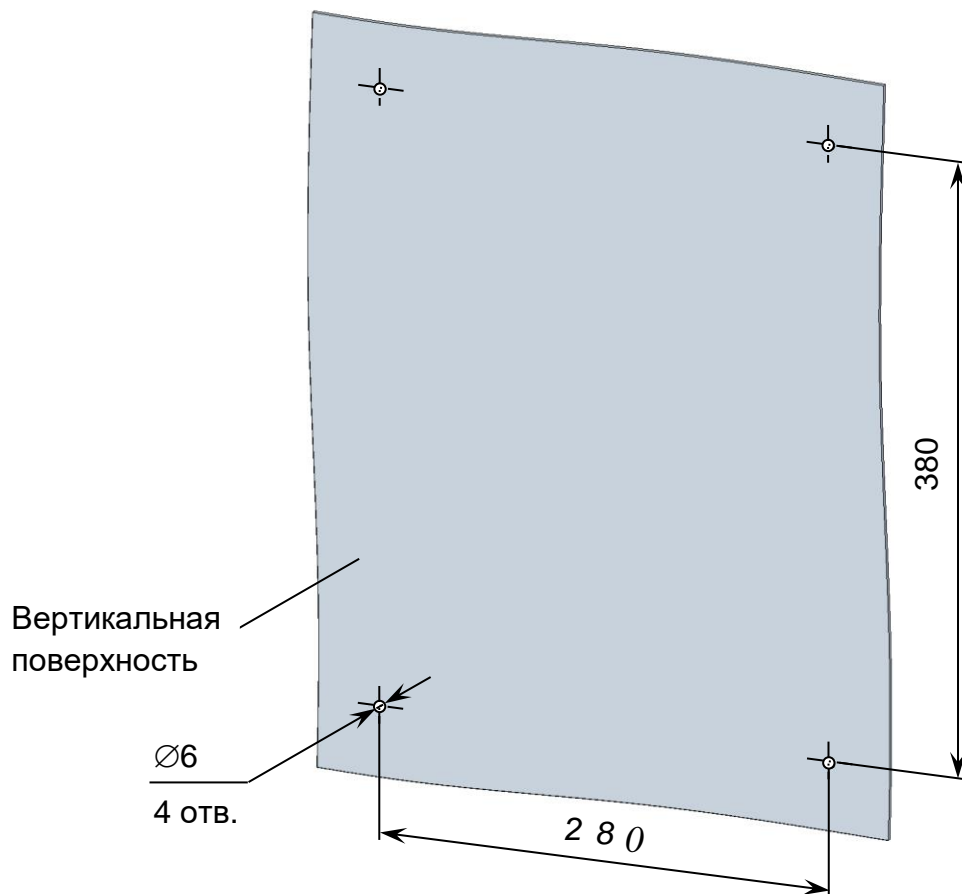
Расположение и размер отверстий для крепления гидропанели
